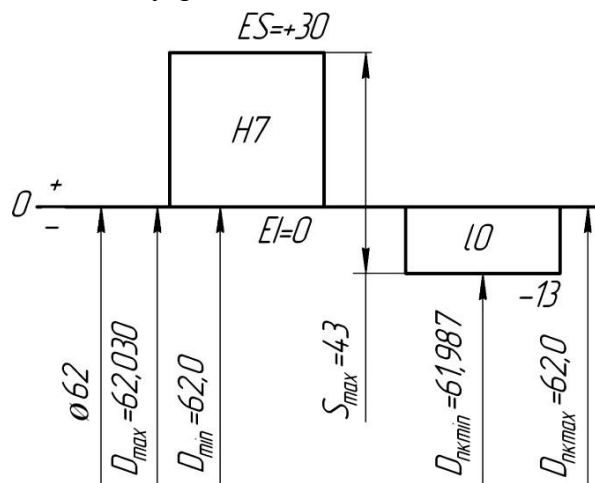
Схема расположения полей допусков сопряжения отверстие корпуса – наружное кольцо подшипника
